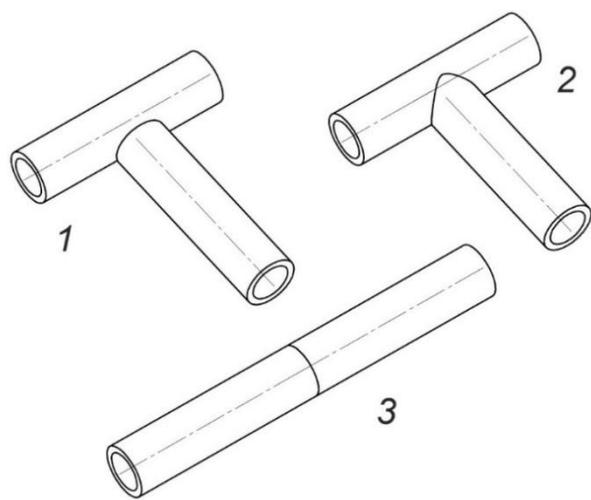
Виды сварных стыковок труб в раме квадроцикла
